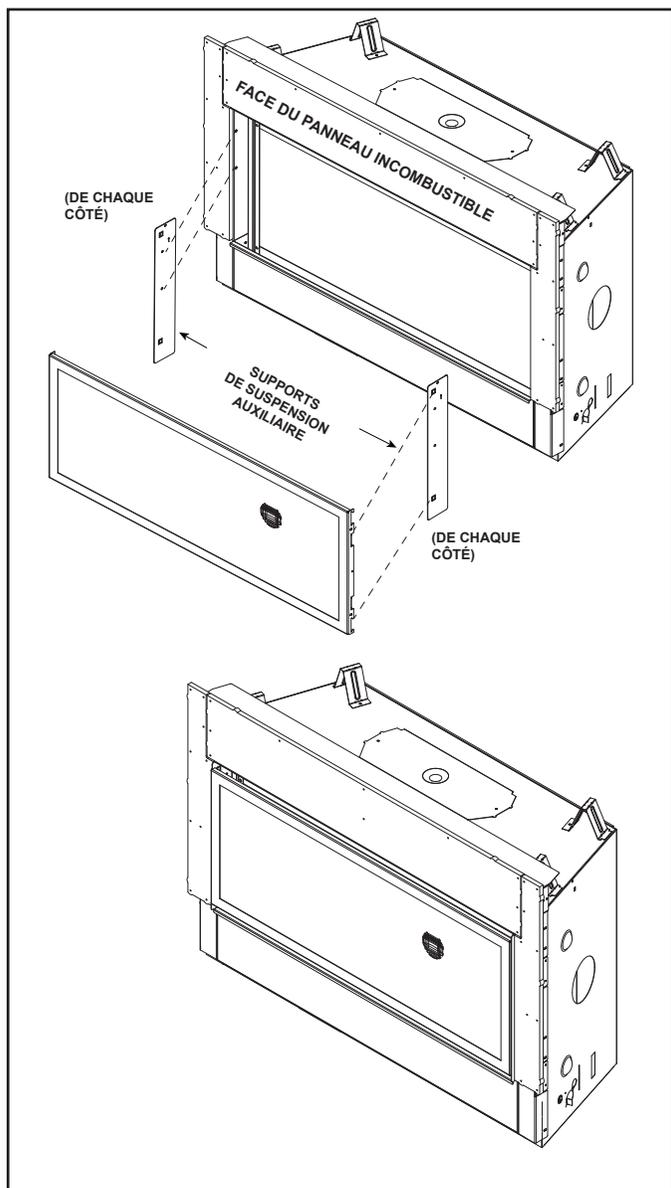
Façade CFT sans la moulure externe de la façade décorative
